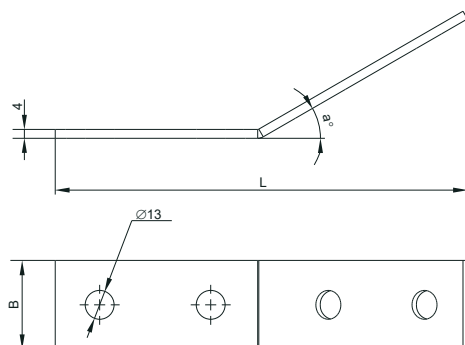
Уголок крепежный наклонный для STRUT-профиля / Figure F.4 – Inclined fastening angle for STRUT profile
